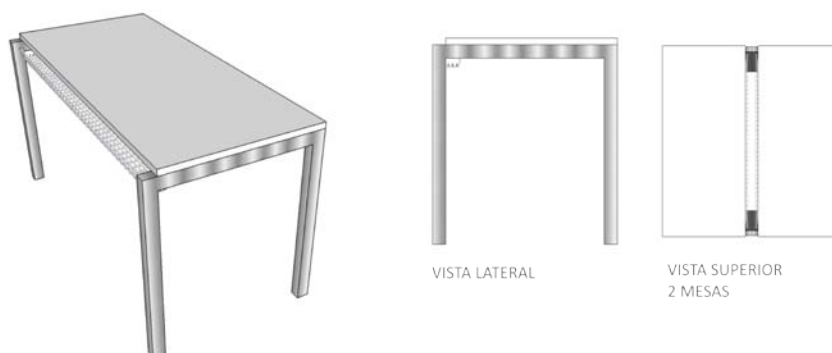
Alternativa para tampo da mesa de trabalho. Fonte: Autora.
